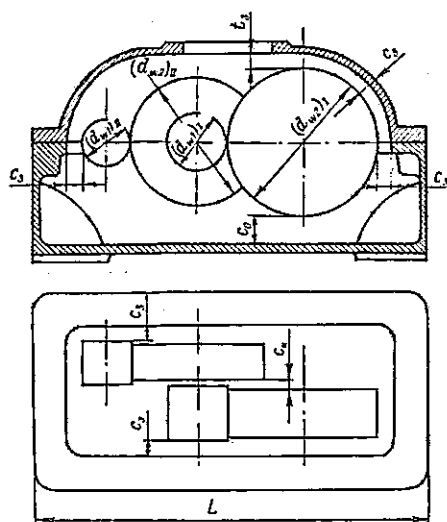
Зазоры между вращающимися деталями и стенками корпуса редуктора
